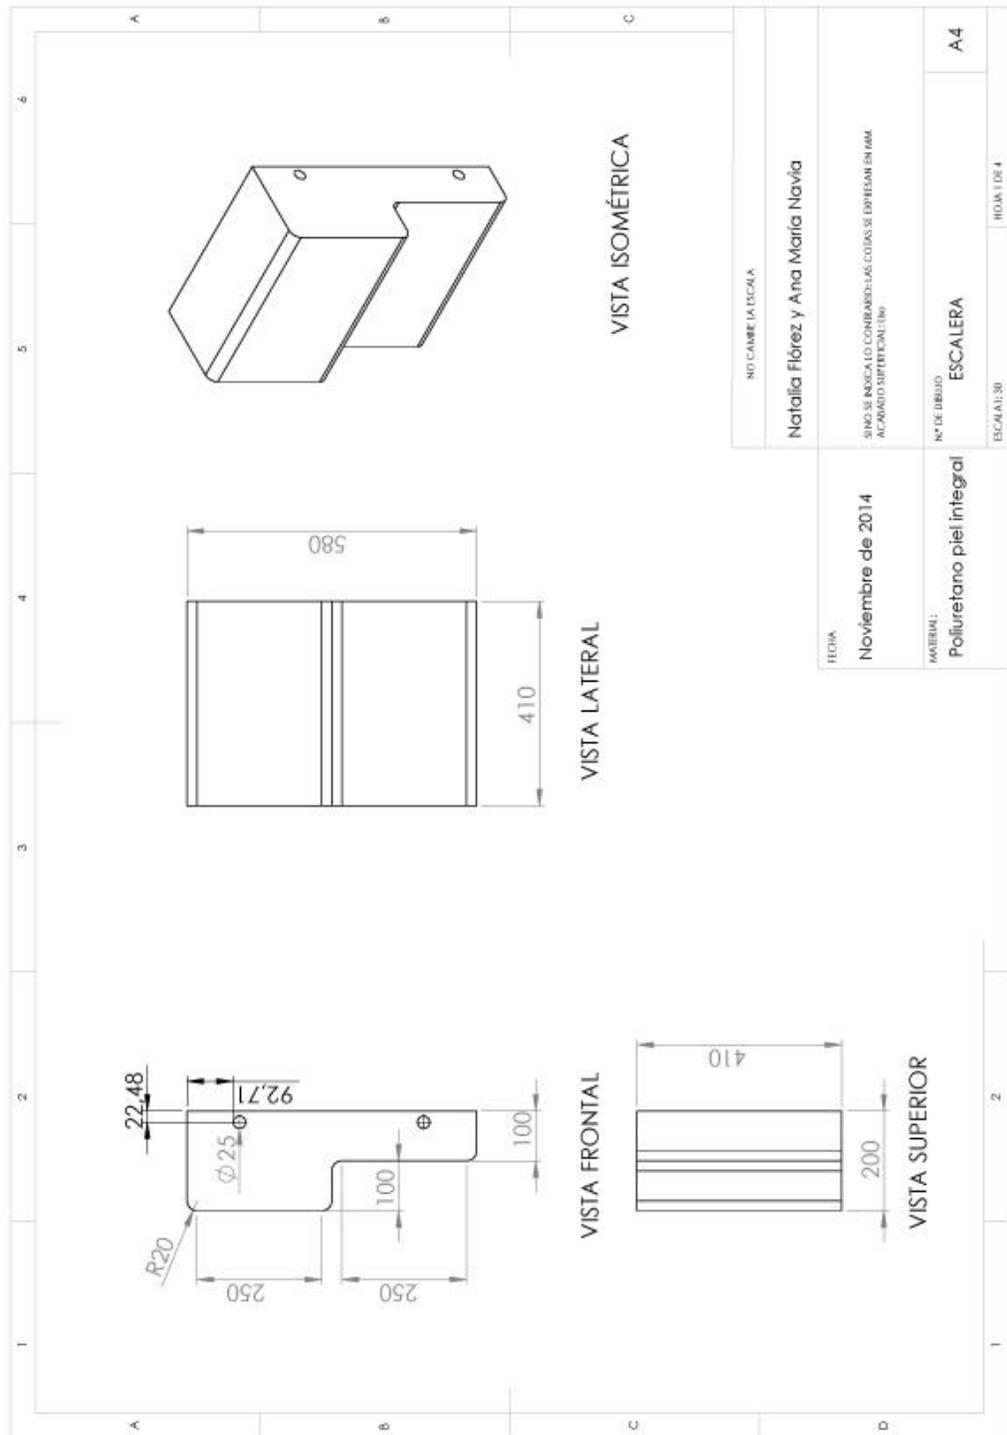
Plano de escalera Fuente: Flórez, N. Navia, A. (2014)
